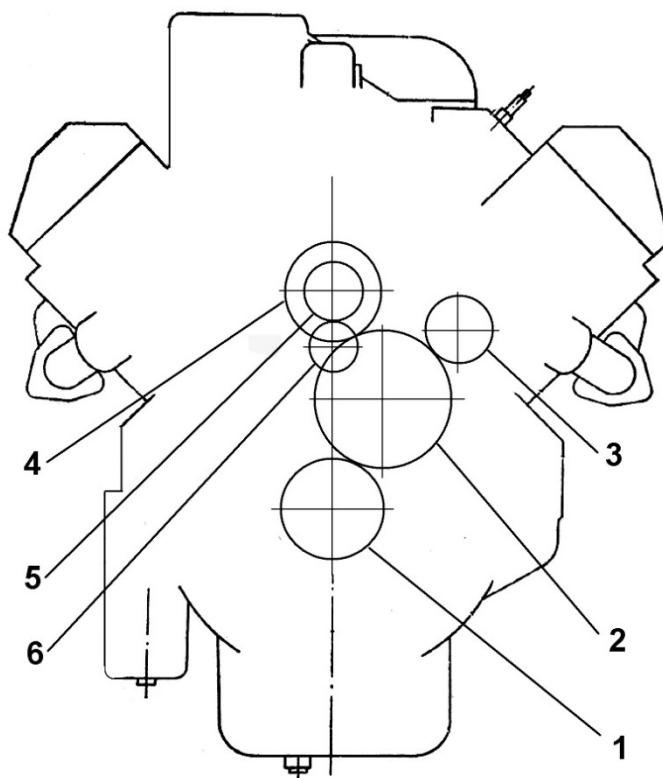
Шестерни привода водяного насоса и вентилятора
